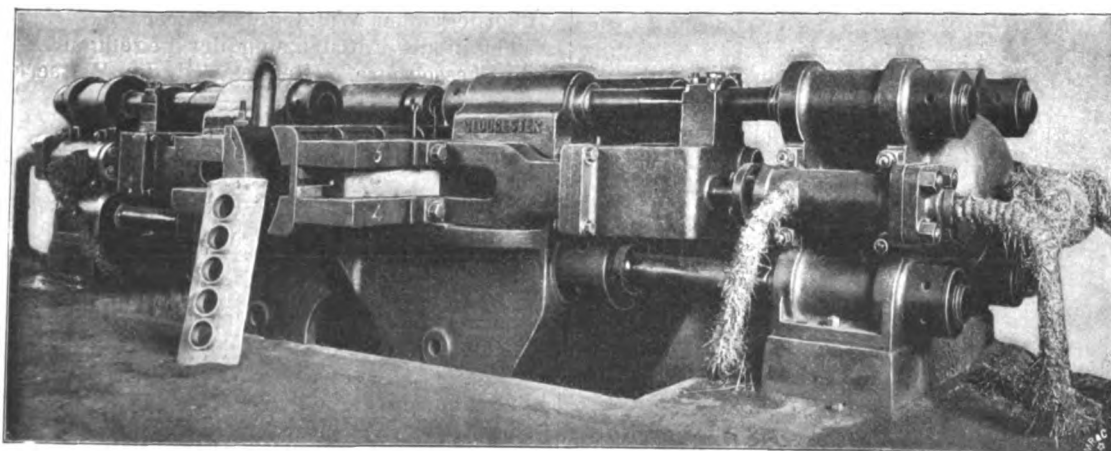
Fräsmaschinen zur Bearbeitung der Wasserkammern aus Temperguß.
